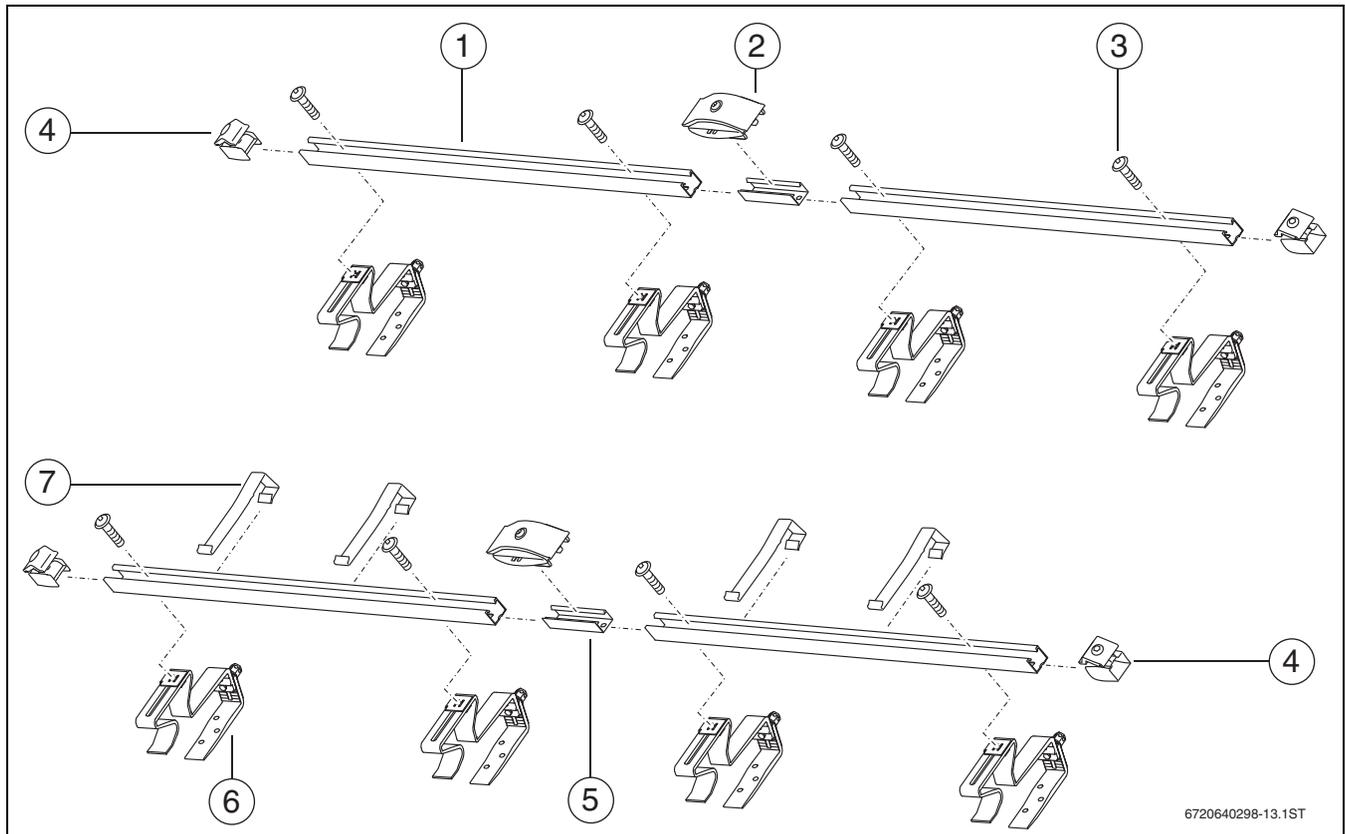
Montage-Set für 2 Kollektoren: 1 Montage-Set Grundausführung, 1 Montage-Set Erweiterung und 2 Montage-Sets für Dachziegel
